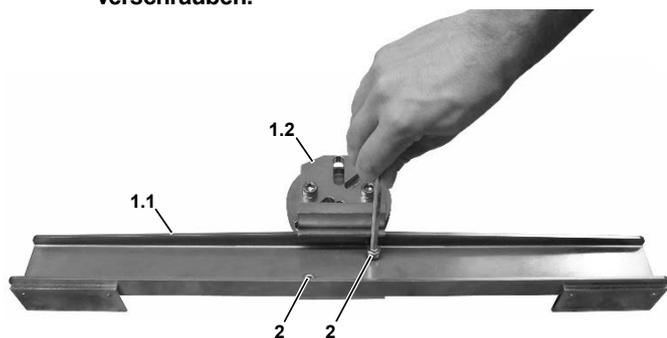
Profilschiene "1.1" mit Grundplatte "1.2" in Schraubstock einspannen.
